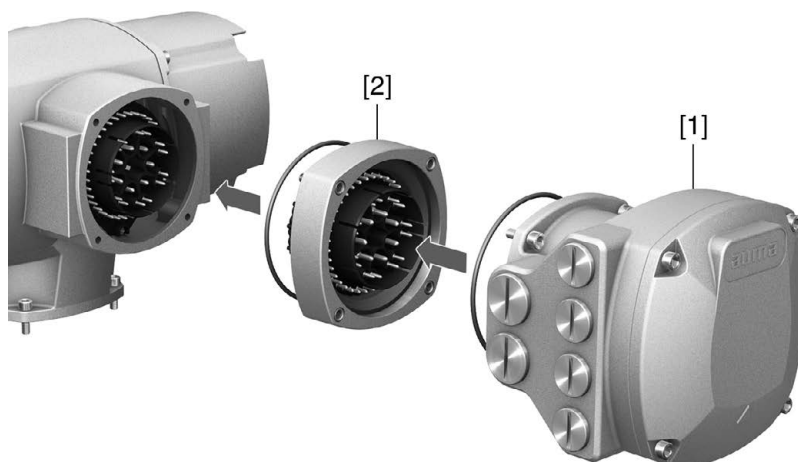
Halterahmen, Beispiel mit AUMA Rundsteckverbinder und Deckel
